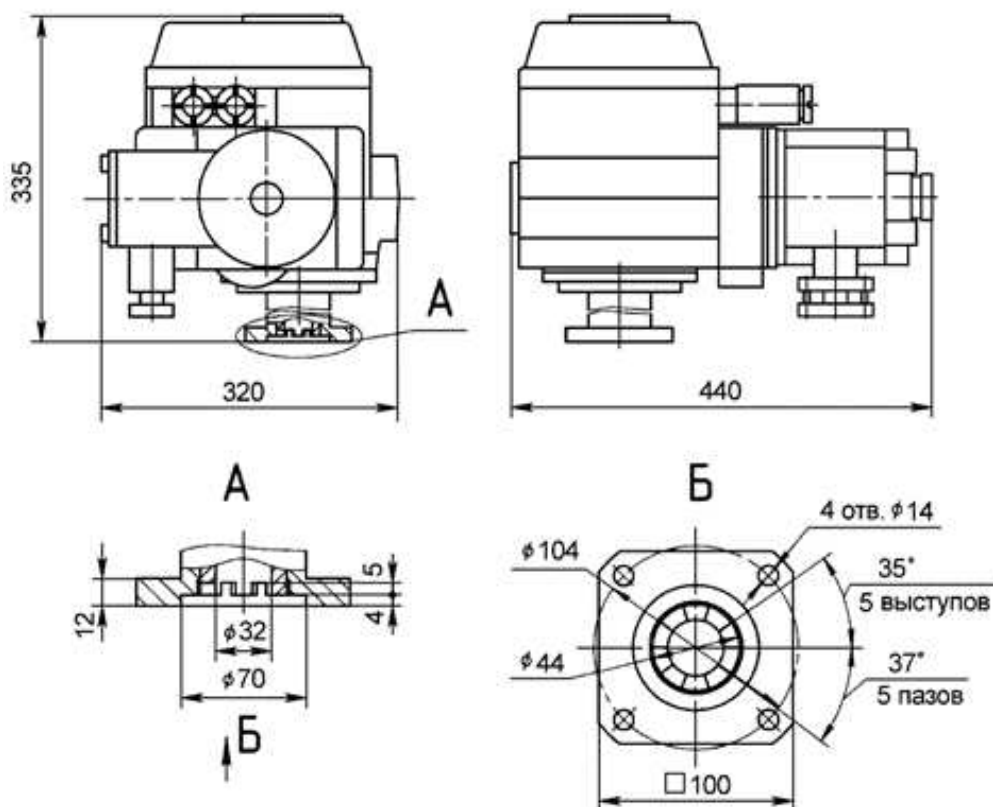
Механізм виконавчий електричний багатооборотний МЭМ-100/160-4 - ПВТ4 - 03
